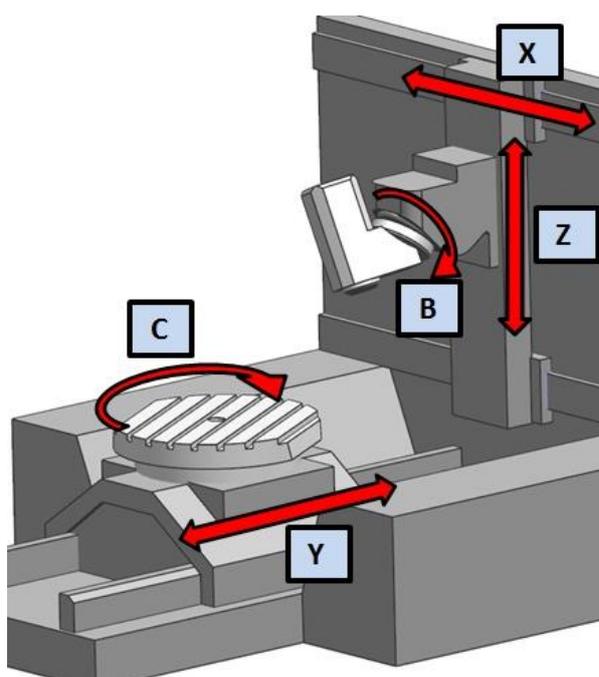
Кинематика 5-ти координатного ОЦ с поворотной фрезерной головкой (ось В) и вращающимся столом (ось С)
